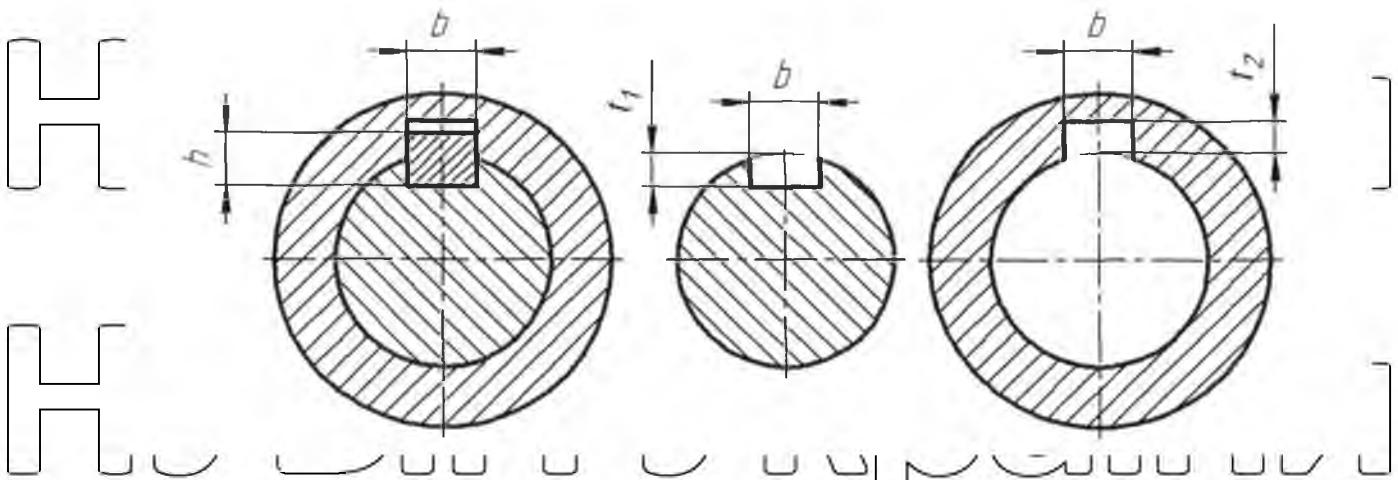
Поперечний переріз шпонкового з'єднання з призматичною шпонкою: h – висота шпонки; b – ширина шпонки; t_1 – виконавча глибина
